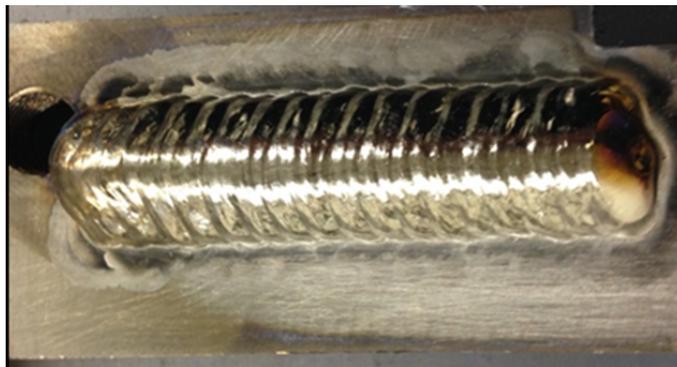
Soudure titane en CMT avec mouvement oscillatoire
